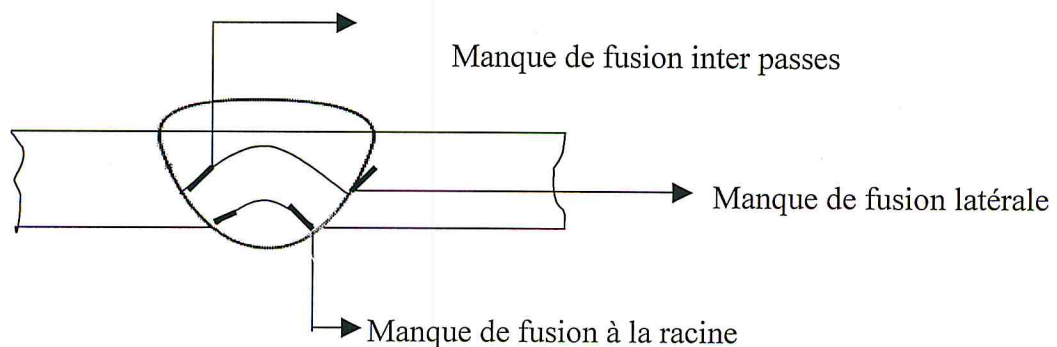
Cordon de soudure présentant un manque de fusion
